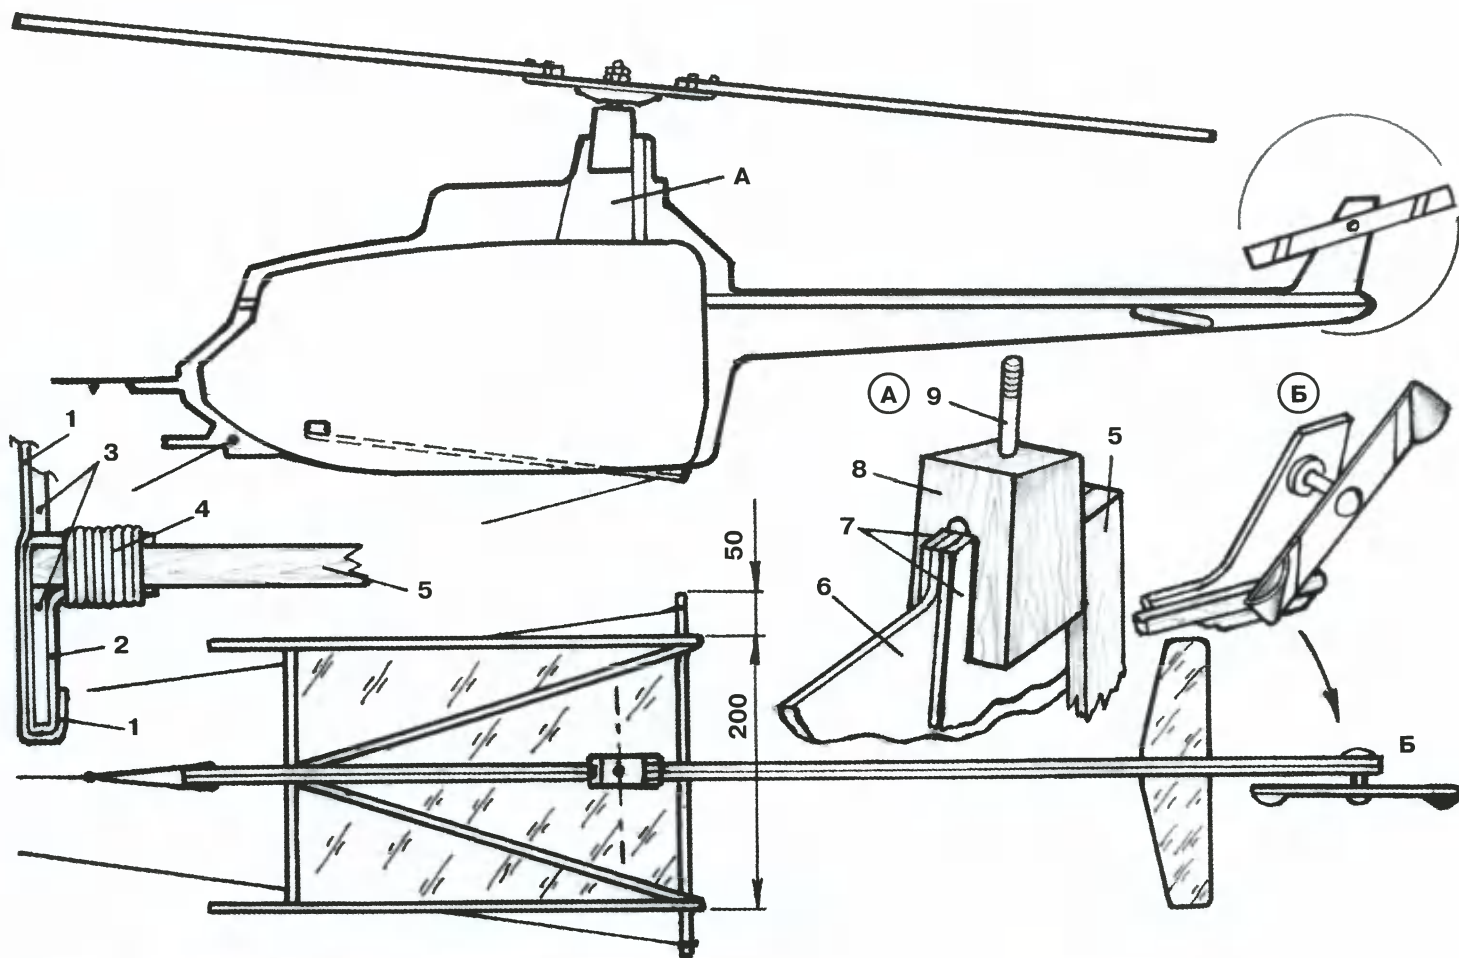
Конструкция модели: 1 — обшивка; 2 — липкая лента; 3 — картон; 4 — биндаж; 5 — рейка; 6 — фюзеляж; 7 — картонные накладки (клеить); 8 — ступица; 9 — ось.
